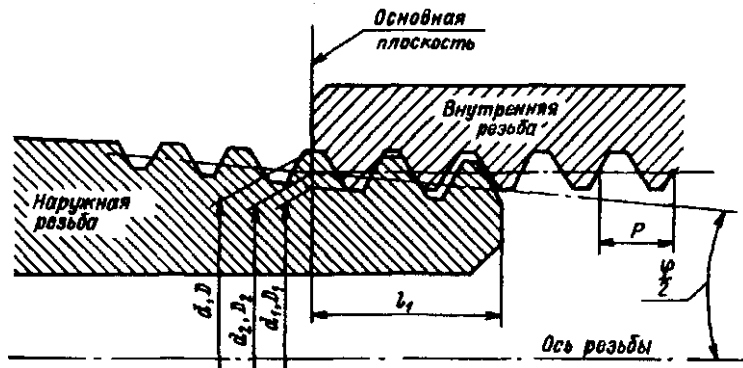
Соединение наружной конической и внутренней цилиндрической резьб
